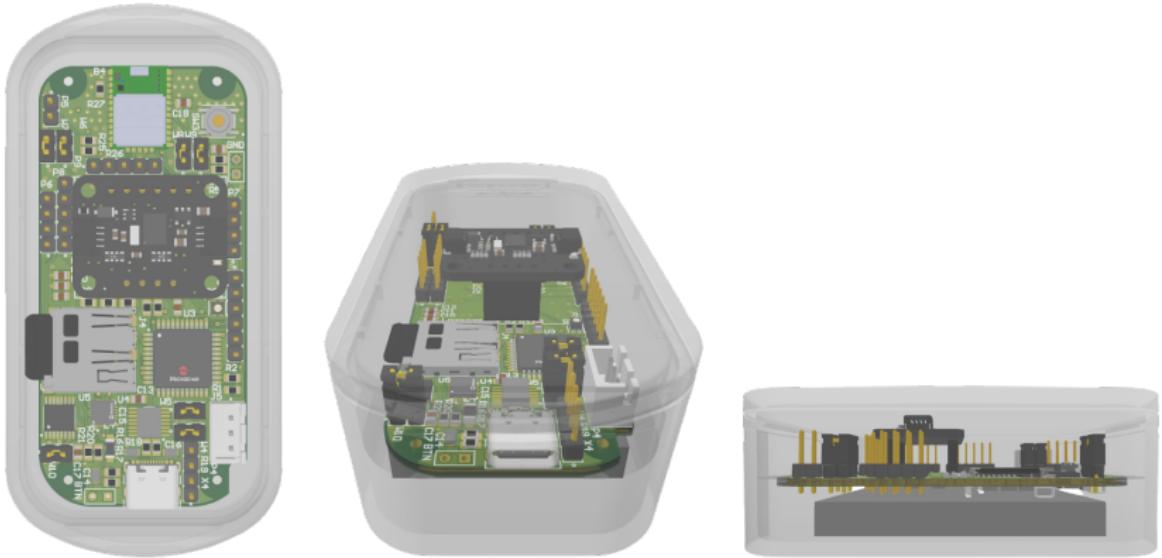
Dimensions du SIC5-9-3B TAKACHI.
